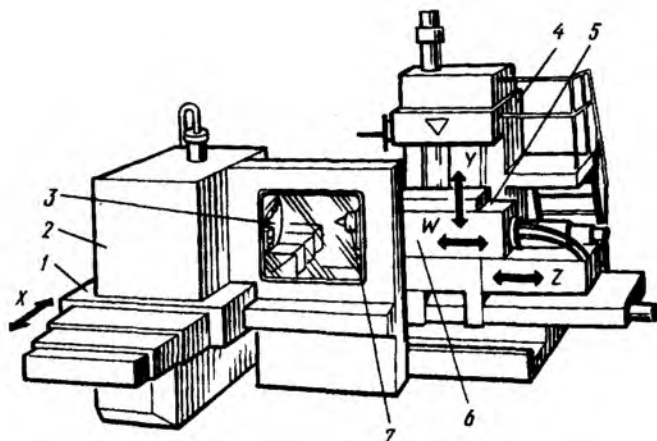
Токарный многоцелевой станок мод. 16A90MФ4: 1, 5 — салазки, 2, 6 — бабки шпиндельные, 3 — патрон, 4 — стойка, 7 — шпиндель инструментальный
